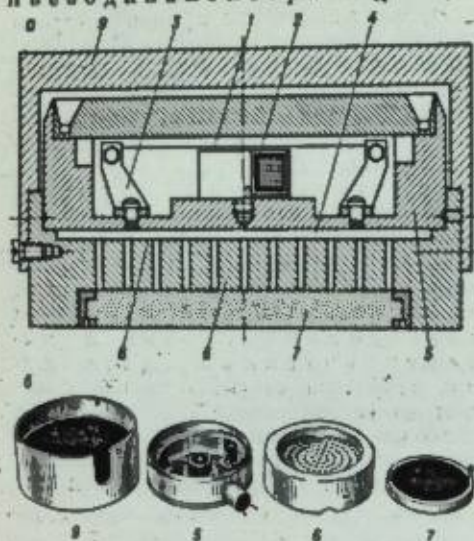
Пьезодинамометр: 1 — измерительная струна; 2 — катушка электромагнита; 3 — колпачок; 4 — кольцевая мембрана; 5 — корпус; 6 — решетка; 7 — пористый напесток; 8 — солидол; 9 — защитный конус.
